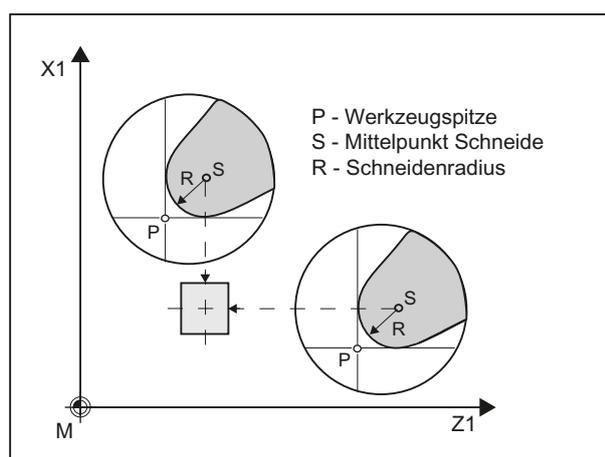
Drehwerkzeug Länge messen: Versatz um Schneidenradius, Beispiel SL=3
